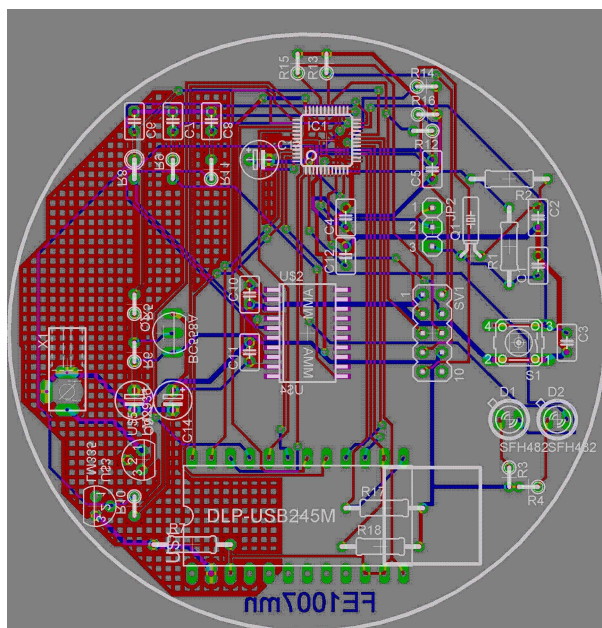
Layout* da PCB do primeiro protótipo da FE.
